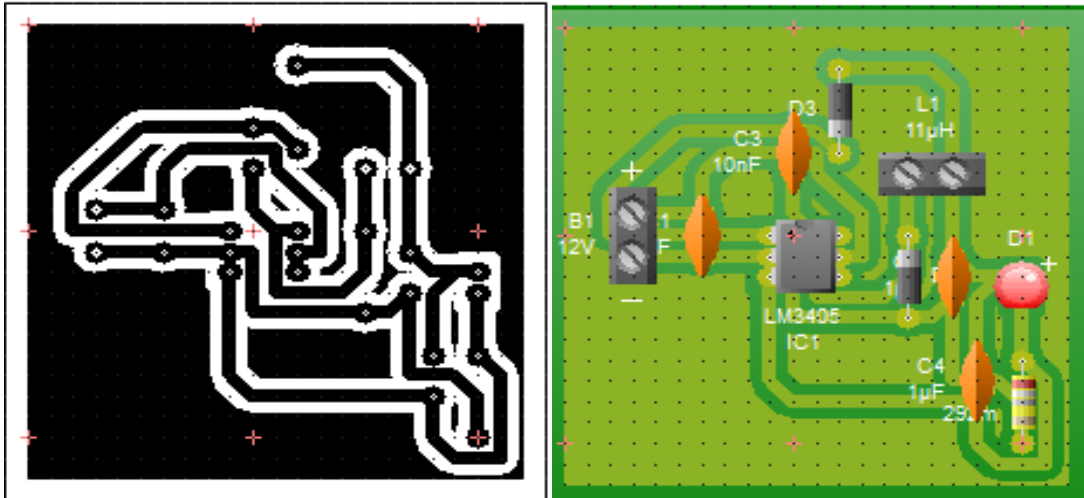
PCB para planchar en placa fenólica y PCB visto en la forma en que se vería físicamente.
